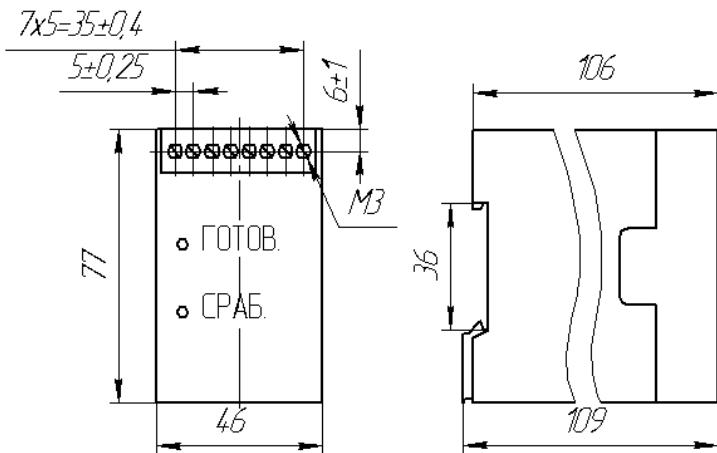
Габаритные, установочные и присоединительные размеры реле РКИ.
